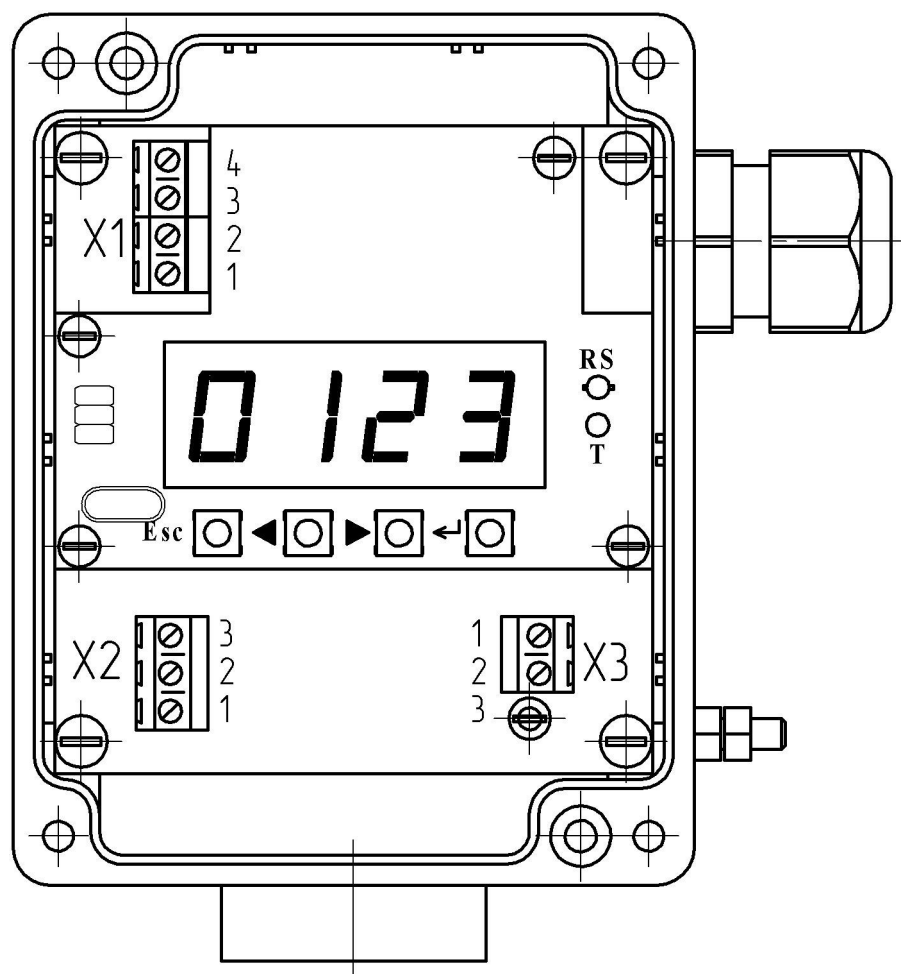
Корпус «Д», вид со стороны передней панели
